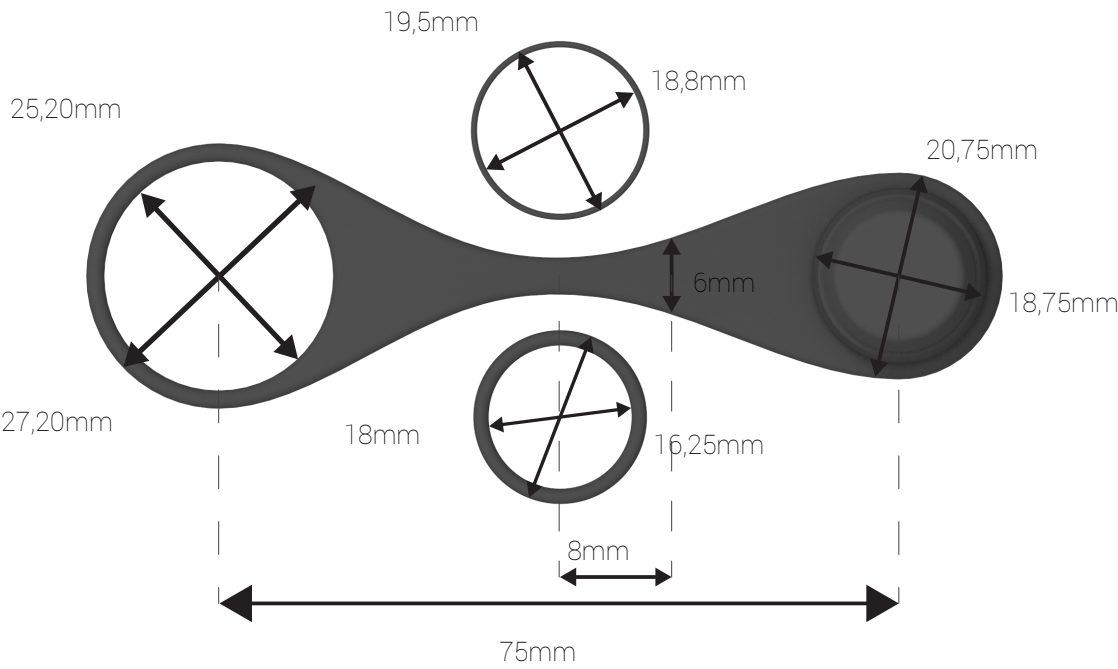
Planos de construcción de la propuesta para botellas. Elaboración propia
